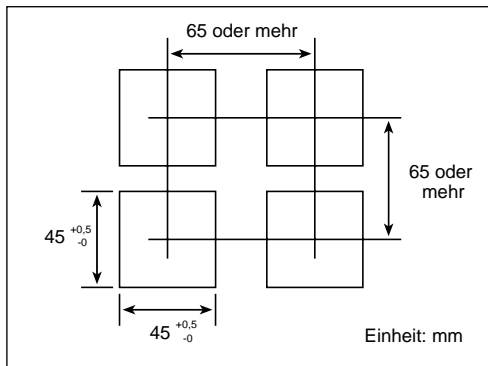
Tafelausschnitt: CN4801 und CN4802 (1/16 DIN)
